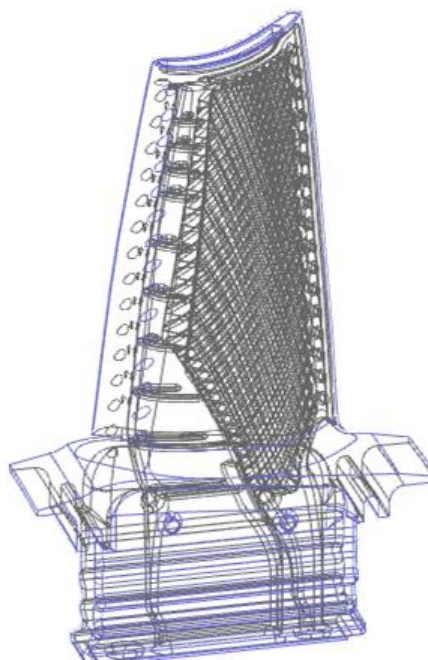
Статический каркас рабочей лопатки ТВД АЛ-31СТ
